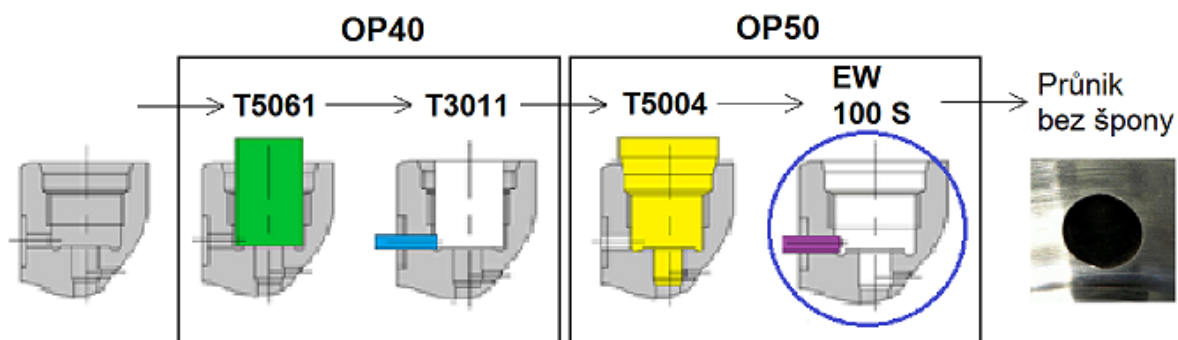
Způsob funkce odhrotovací spirály EW 100 S [2].
